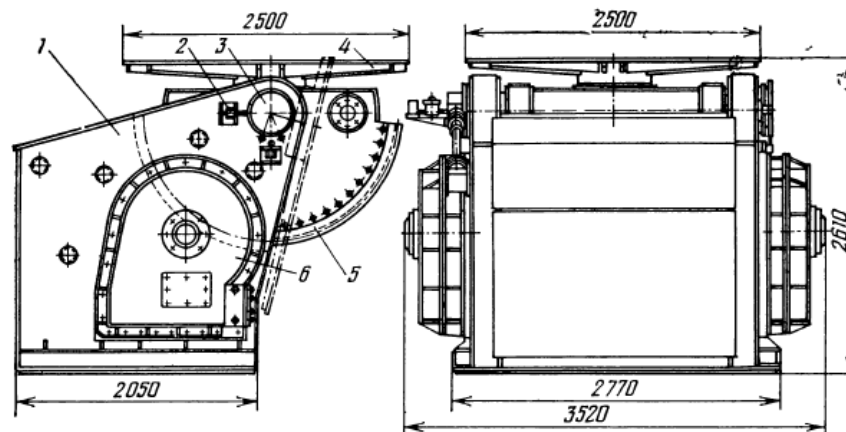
Схема конструкції зварювального маніпулятора Т-25М
